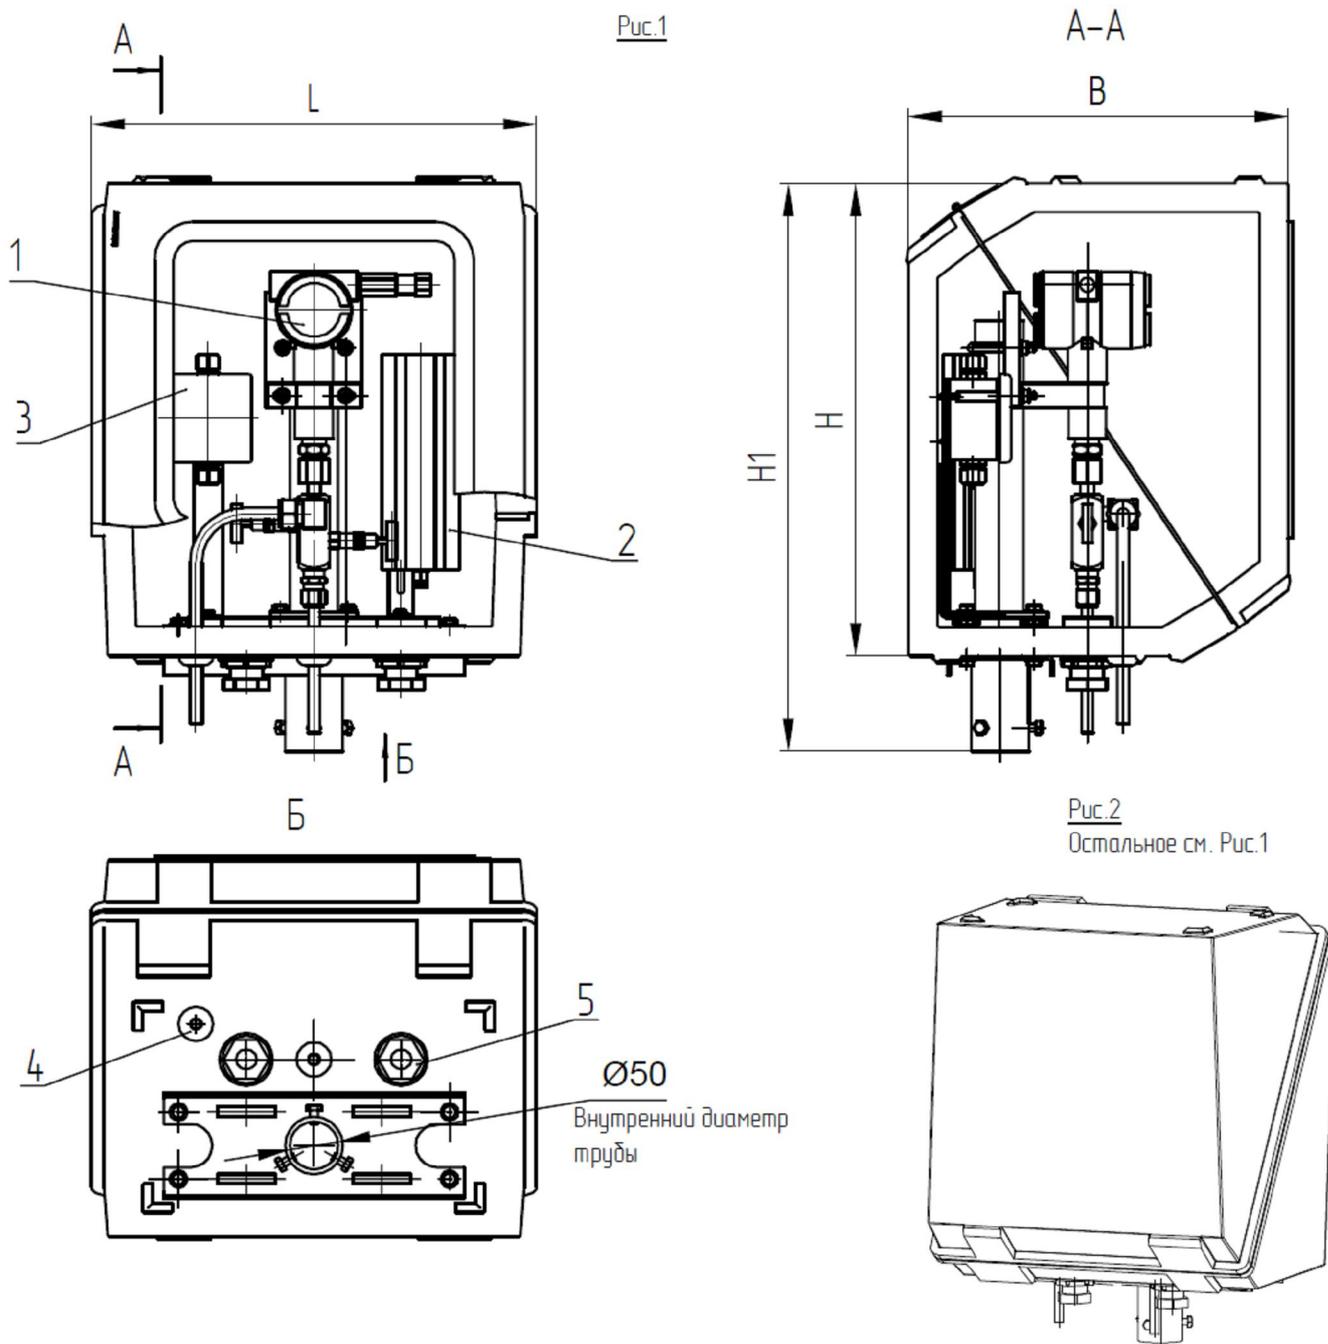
Габаритные и установочные размеры шкафов ШПУЭЗ-Р-О-Н, ШПУЭЗ-Р-Г-Н
